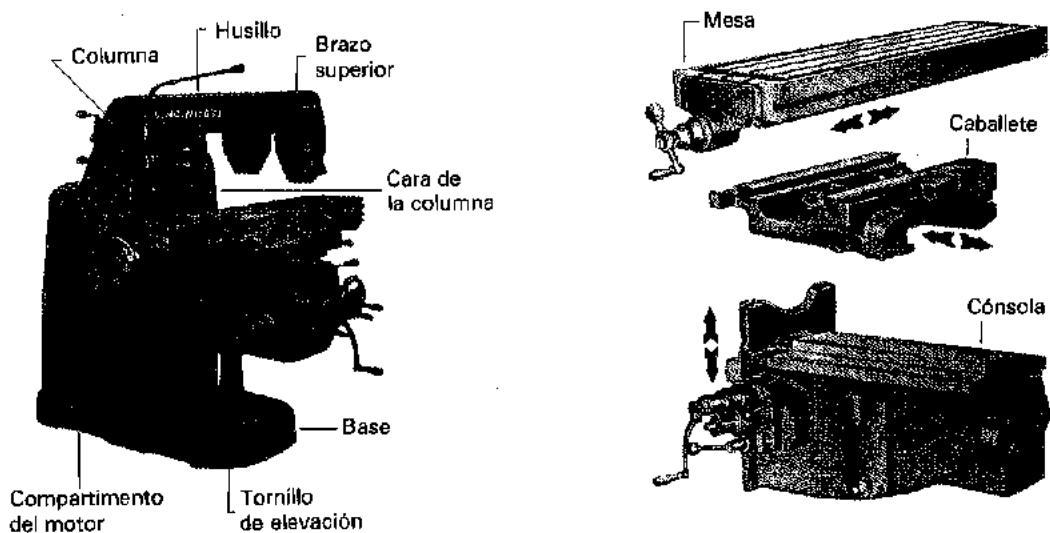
Partes principales de la fresadora corriente de columna y cartela (Cincinnati Milling Machine Co.)
